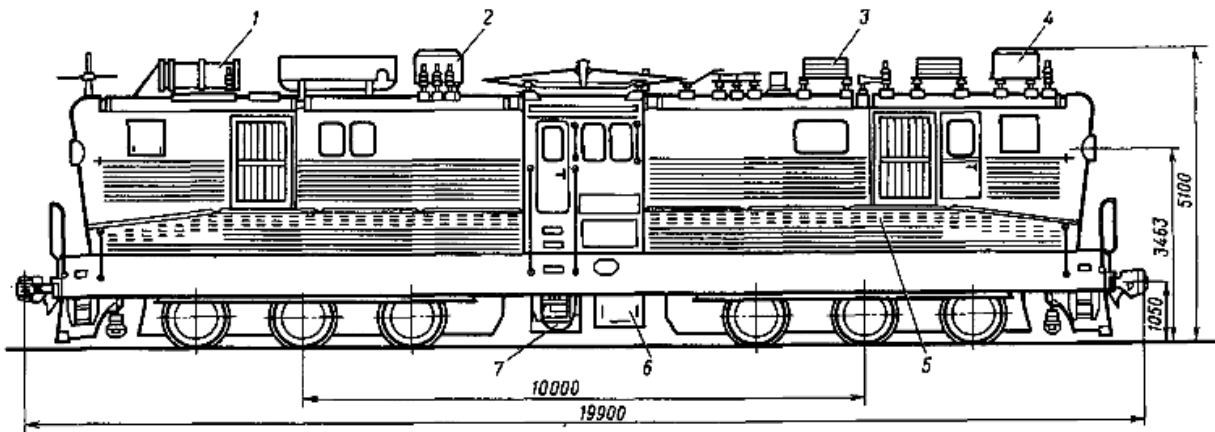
Электровоз серии ВЛ26: 1,6 – сглаживающие реакторы, 2 – демпферный резистор мотор- компрессора, 3 – реактор фильтра, 4 – демпферный резистор мотор- вентилятора, 5 –камеры тяговой батареи, 7 – двигатель-генератор
